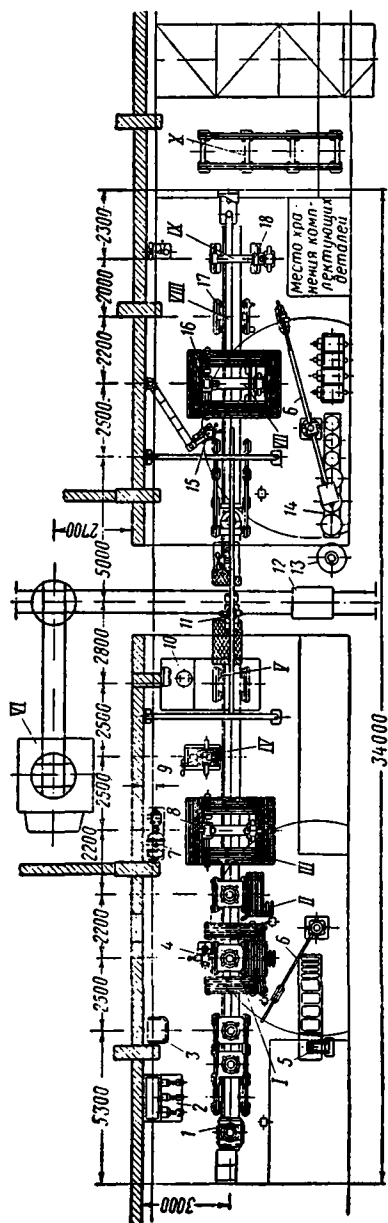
Схема поточно-конвейерной линии для сборки тяговых двигателей типа ЭДТ-200.
